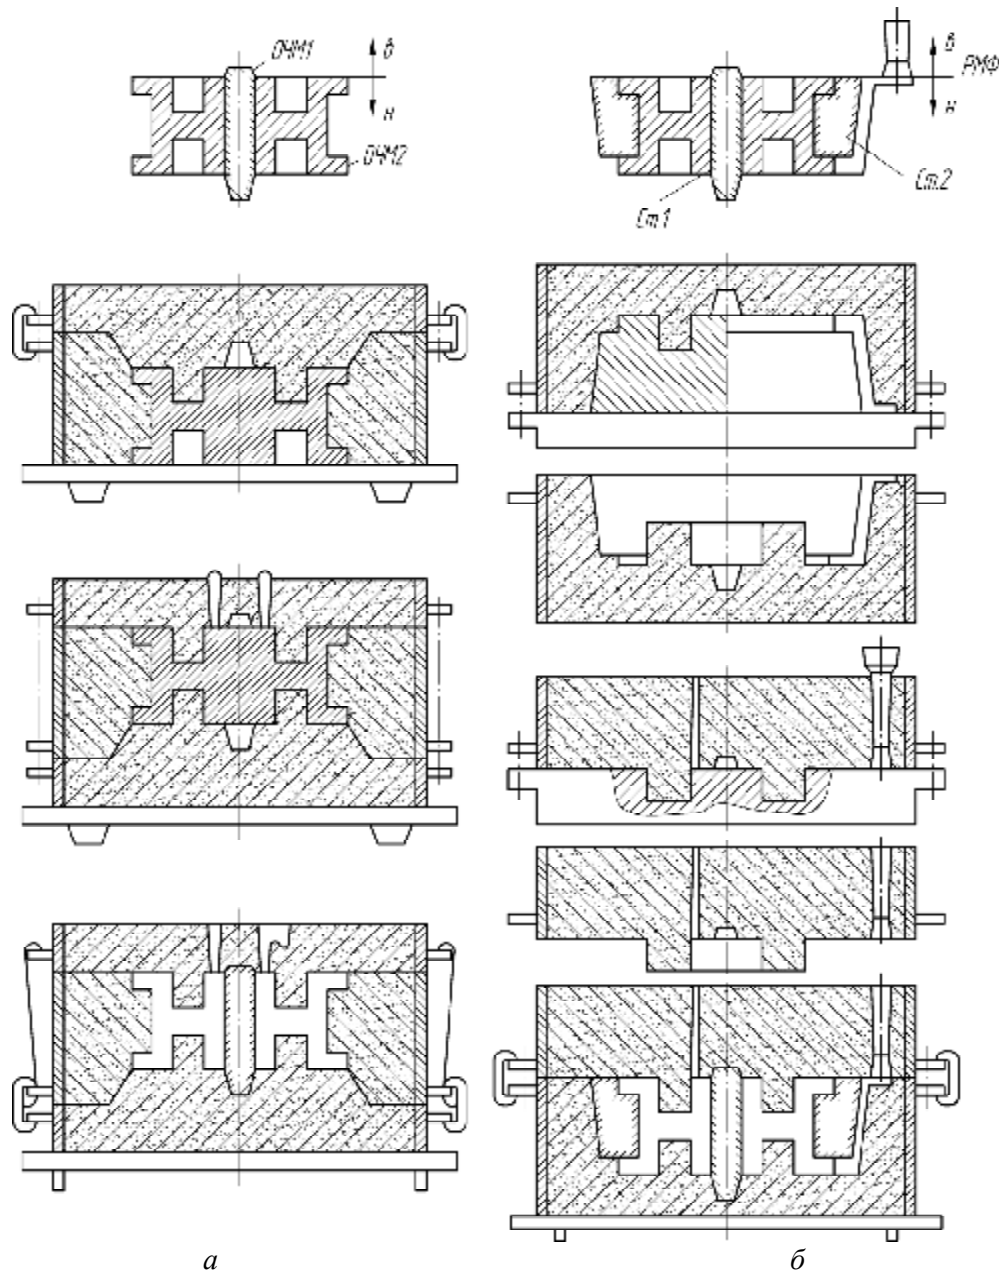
Схемы изготовления формы для отливки шкива вручную (а) и на машинах (б)
